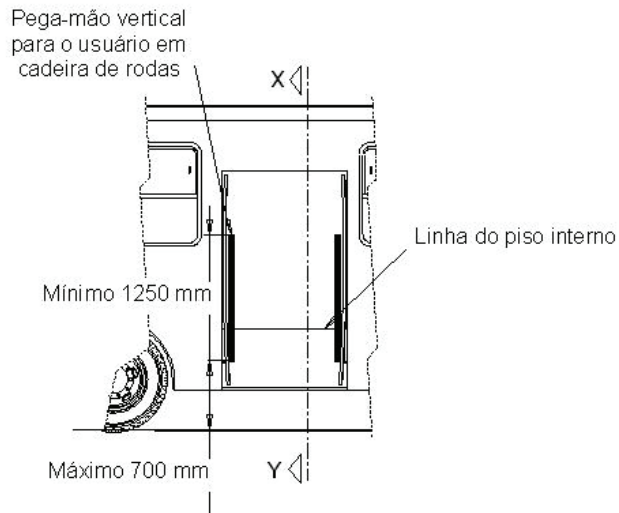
Pega-mão instalado nas folhas de porta (vista frontal)
